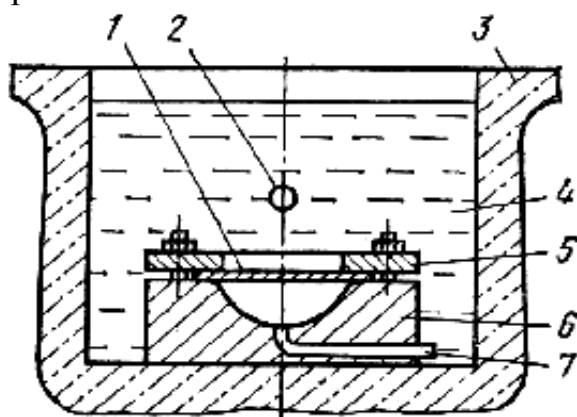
Схема штамповки взрывом деталей из плоской заготовки:
